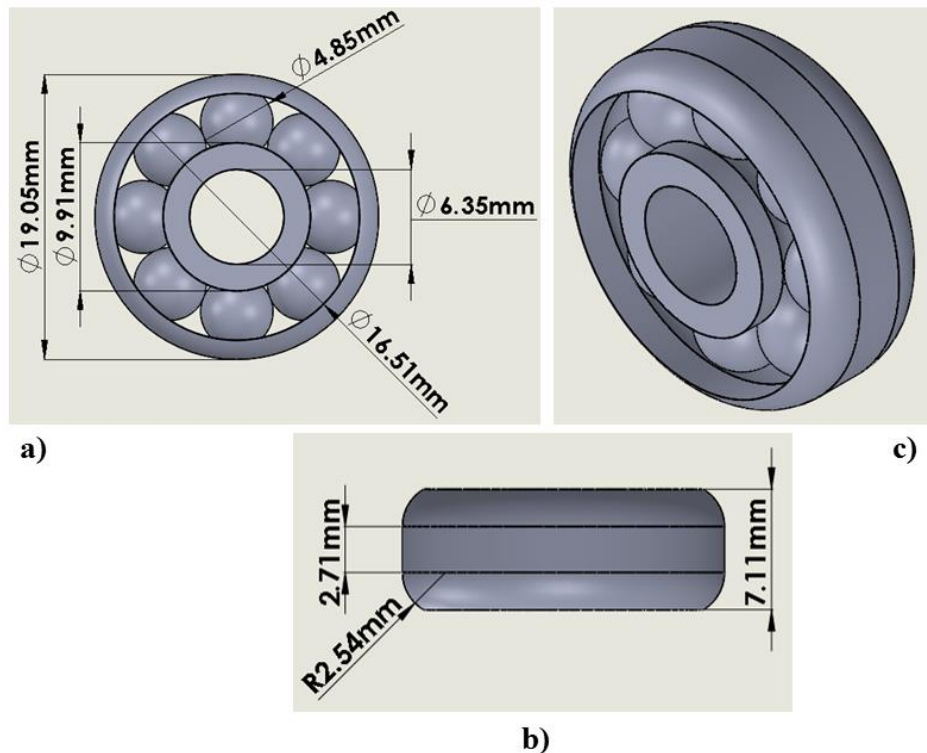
a) Vista frontal del rodamiento de bolas rígidas con sus dimensiones, b) Vista lateral del rodamiento mostrando su espesor, c) Vista isométrica del rodamiento.
